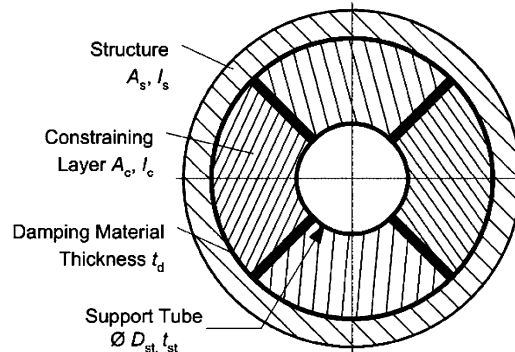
Smorzatore ShearDamper basato sul "constrained layer damping" [Bam02]
